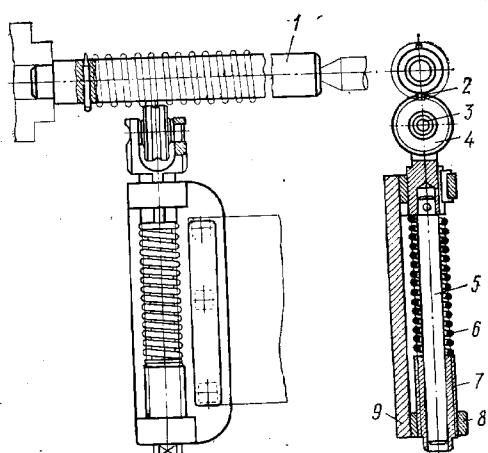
Приспособление для восстановления упругости клапанных пружин
